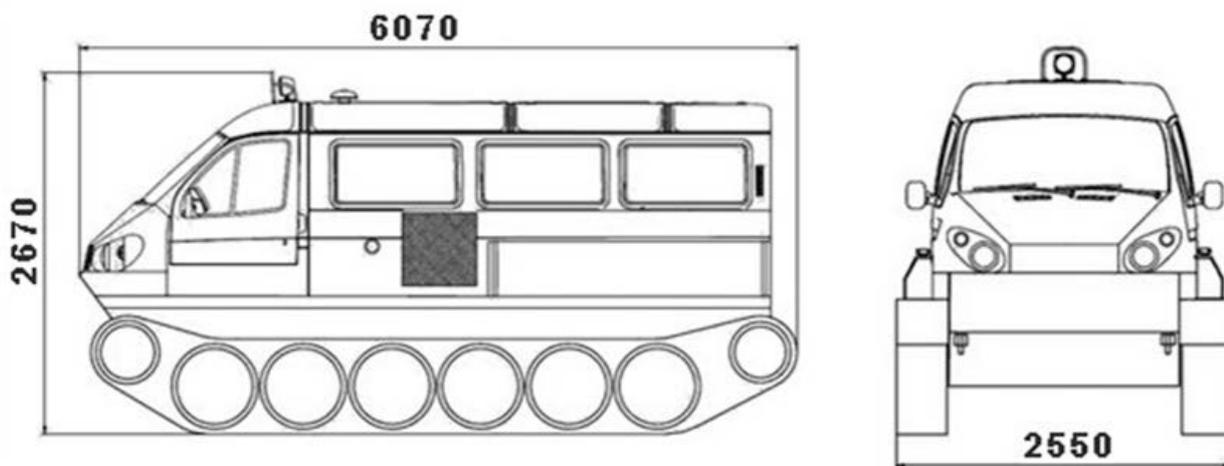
Габаритные размеры ГАЗ-34039 "Ирбис"
